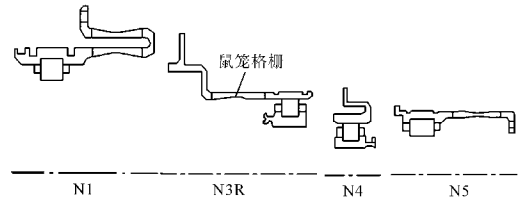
GE90-115B 发动机带弹性支座的滚棒轴承
